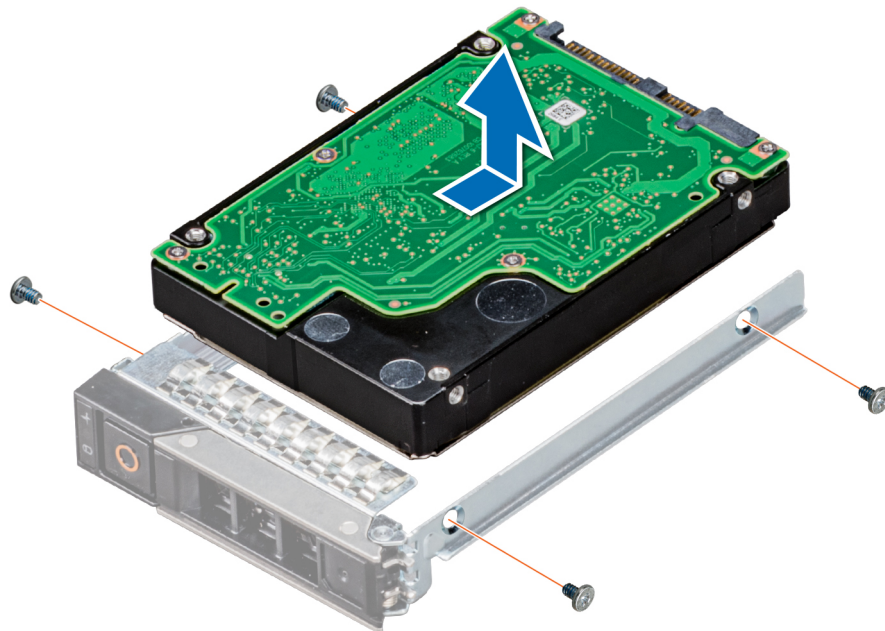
Laufwerk aus Laufwerksträger entfernen
